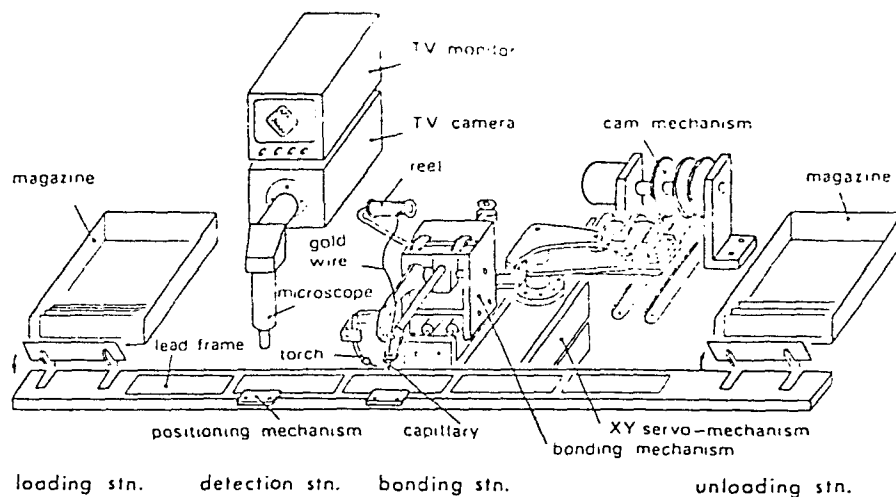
Sistema automatico de soldadura para transistores.
